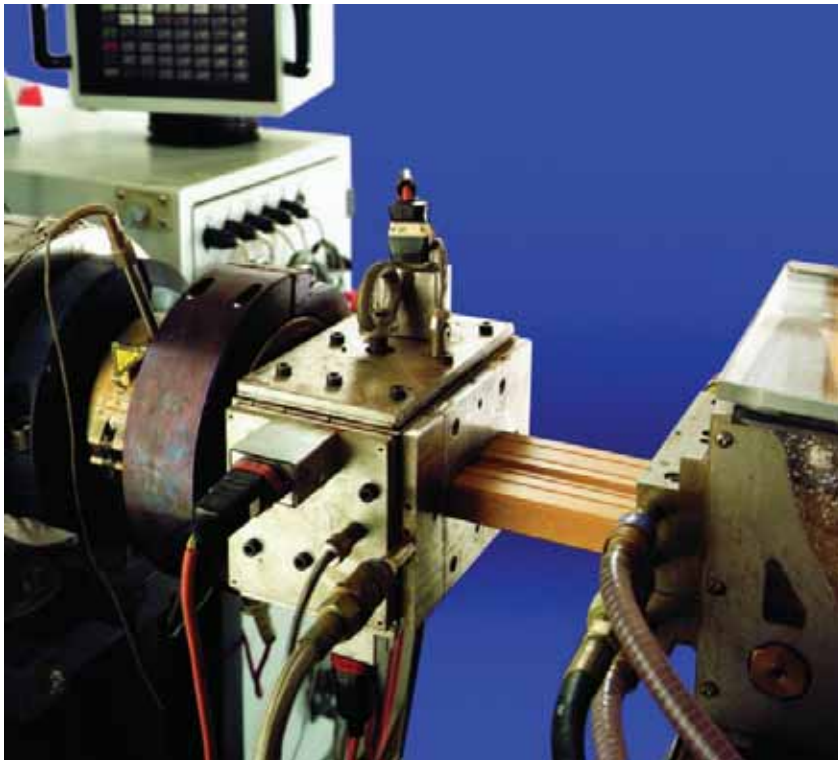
Extrusionswerkzeug mit austretendem Profil
